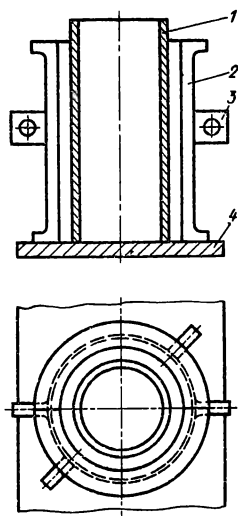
Приспособление для вертикальной заливки баббитом вкладышей:
